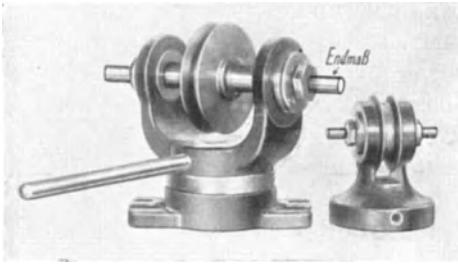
Schwenkvorrichtung zum Schleifen von Kugelendmaßen.
